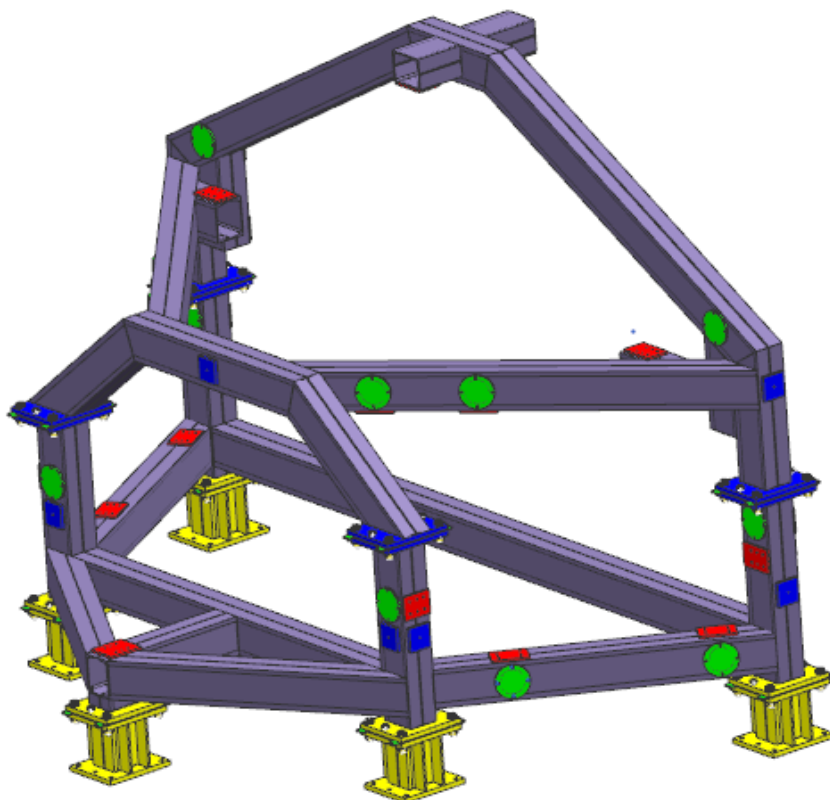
Общий вид каркаса сборного приспособления (изометрия).
